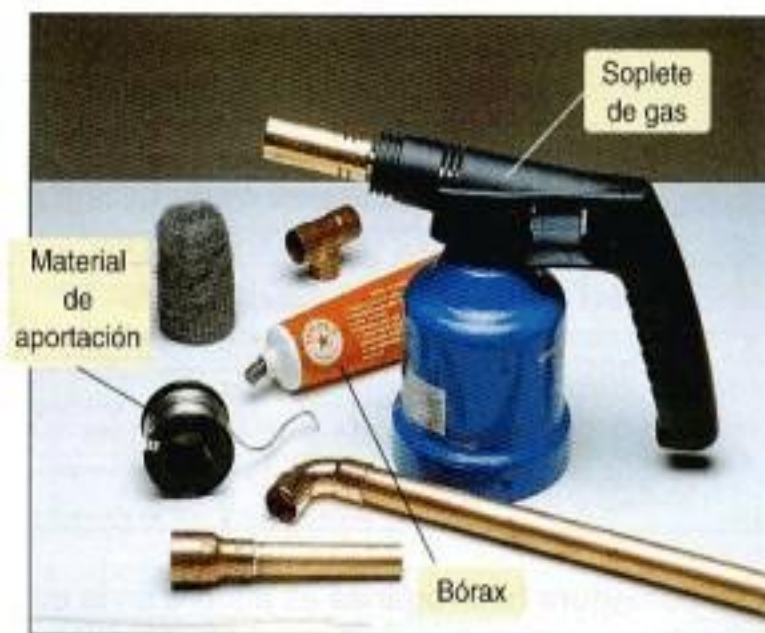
ELEMENTOS DE SOLDADURA BLANDA
